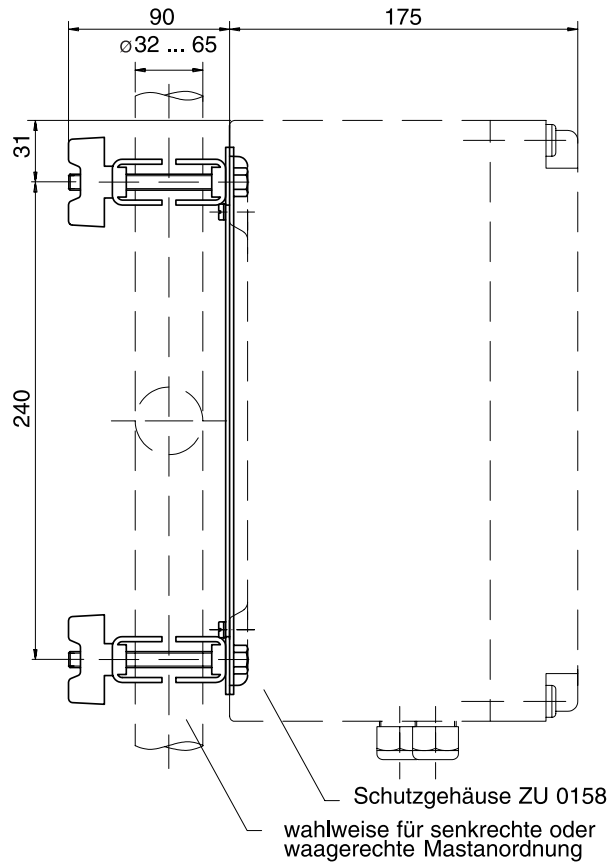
Mastschellensatz ZU 0220 für Schutzgehäuse ZU 0158
